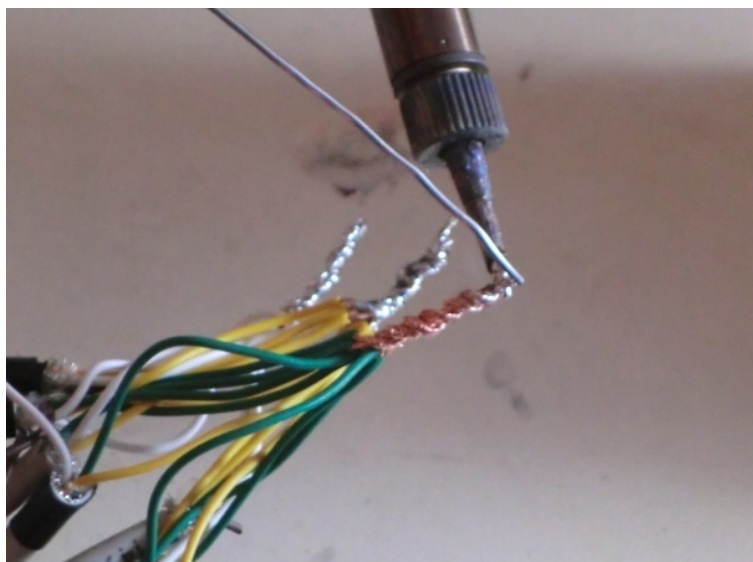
Soldado cableado instalación exterior (1) (elaboración propia)
